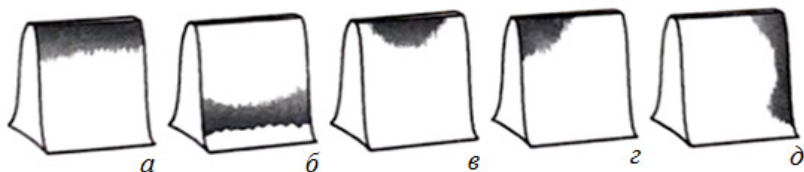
Профили рабочих поверхностей зубьев шестерен: а - легко нагруженной; б - тяжело нагруженной
